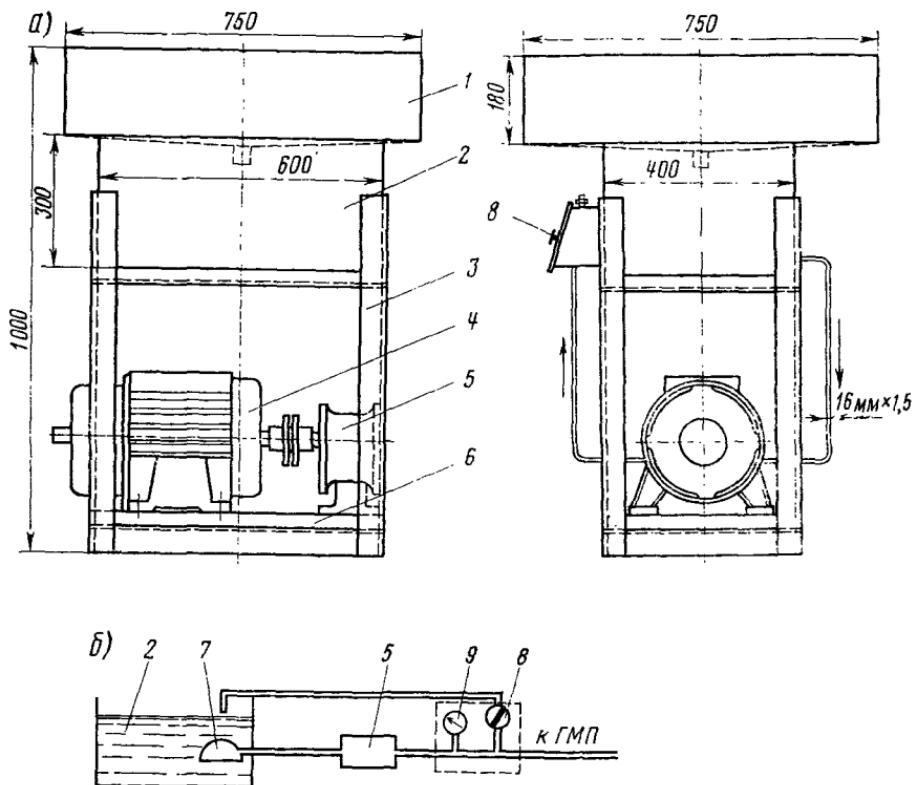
Стенд для проверки узлов гидромеханической передачи на герметичность:
